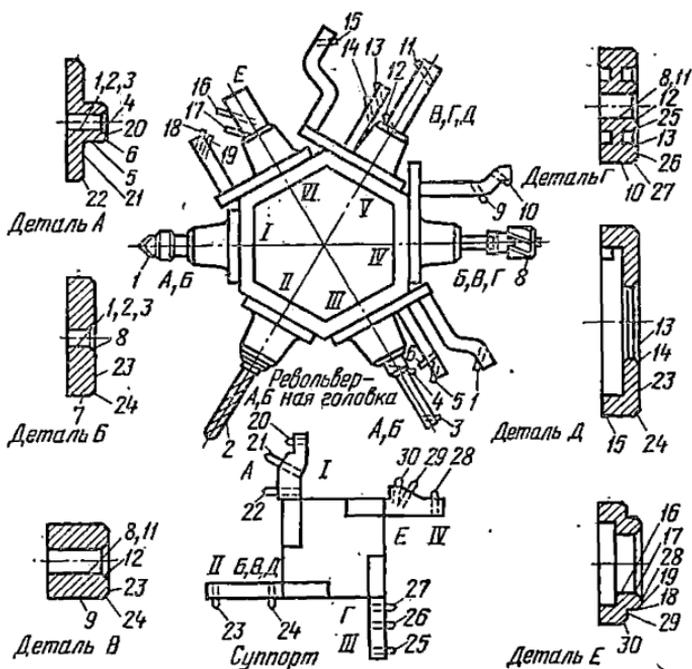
Схема групповой наладки токарно-револьверного станка для обработки заготовок цилиндрических зубчатых колес:
